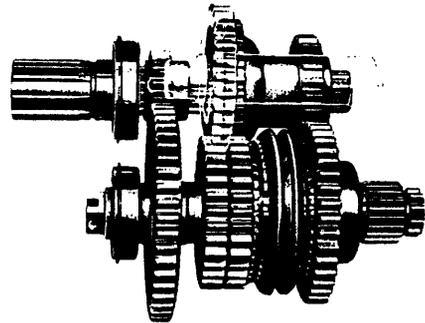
Vue d'ensemble des engrenages de vitesse.
